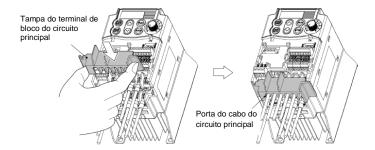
Recolocando a Tampa do Bloco de Terminais (TB)no Circuito Principal
